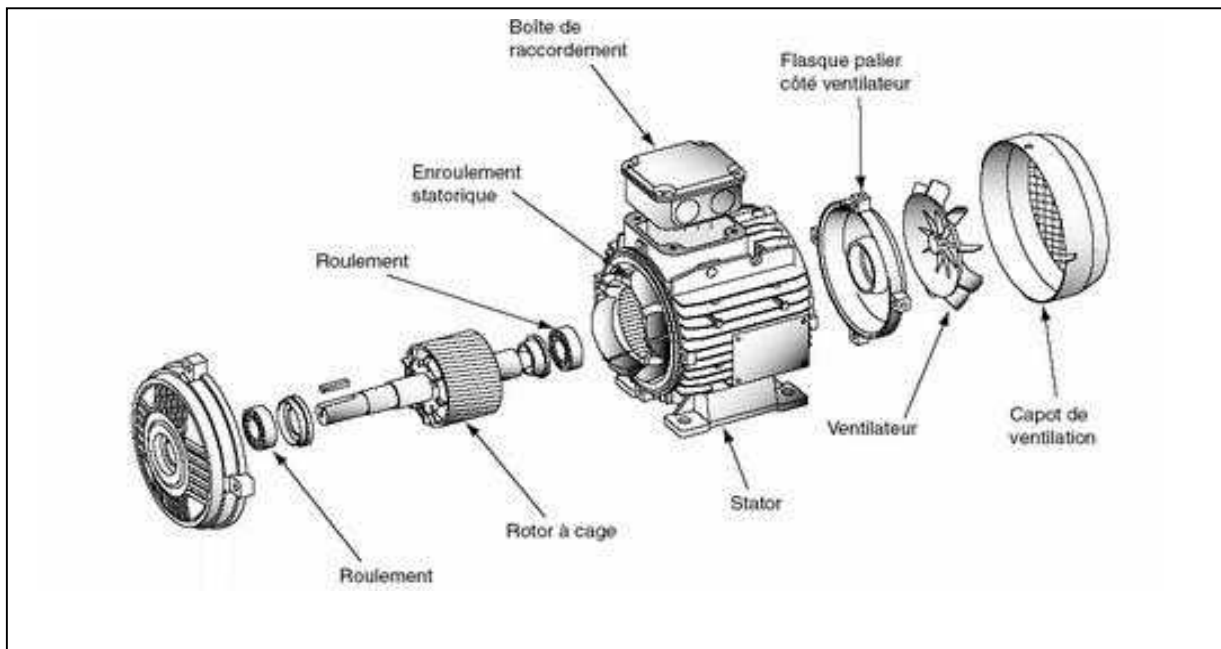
Vue éclatée d'un moteur asynchrone rotor à cage.
